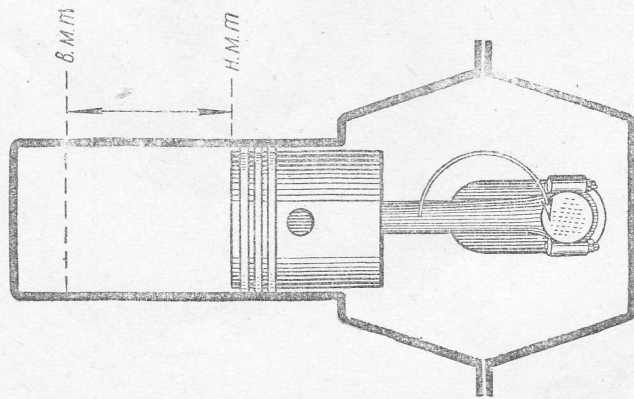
Схема положений поршня в мертвых точках и объем цилиндра.
